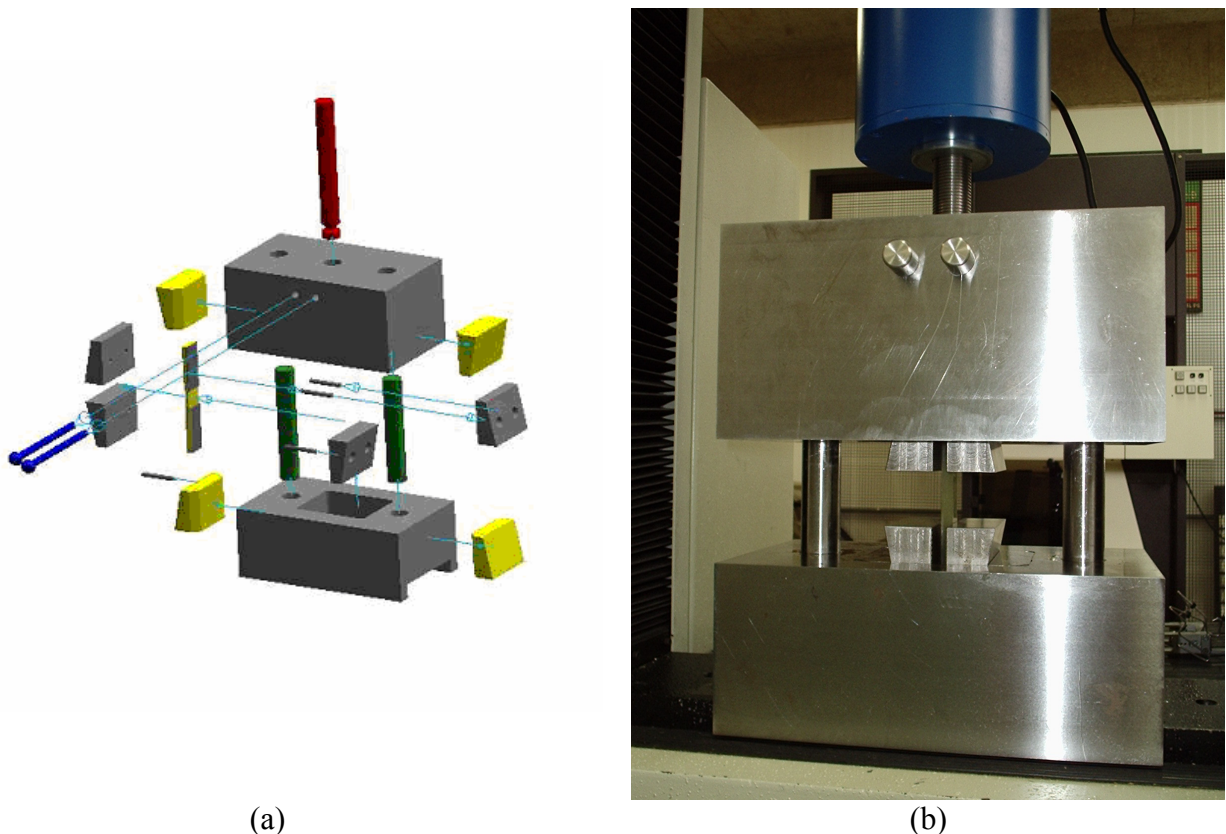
(a) Vista explodida do modelo computacional em Solid Edge® do dispositivo baseado no método IITRI. (b) Dispositivo real montado na máquina de ensaios universal.
